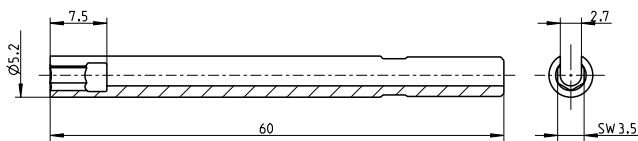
Montageschlüssel Typ 1300A125 für Kabel
